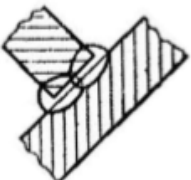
Сварочный процесс выполнения сварного соединения автоматической дуговой сваркой под флюсом (в лодочку) [1]
